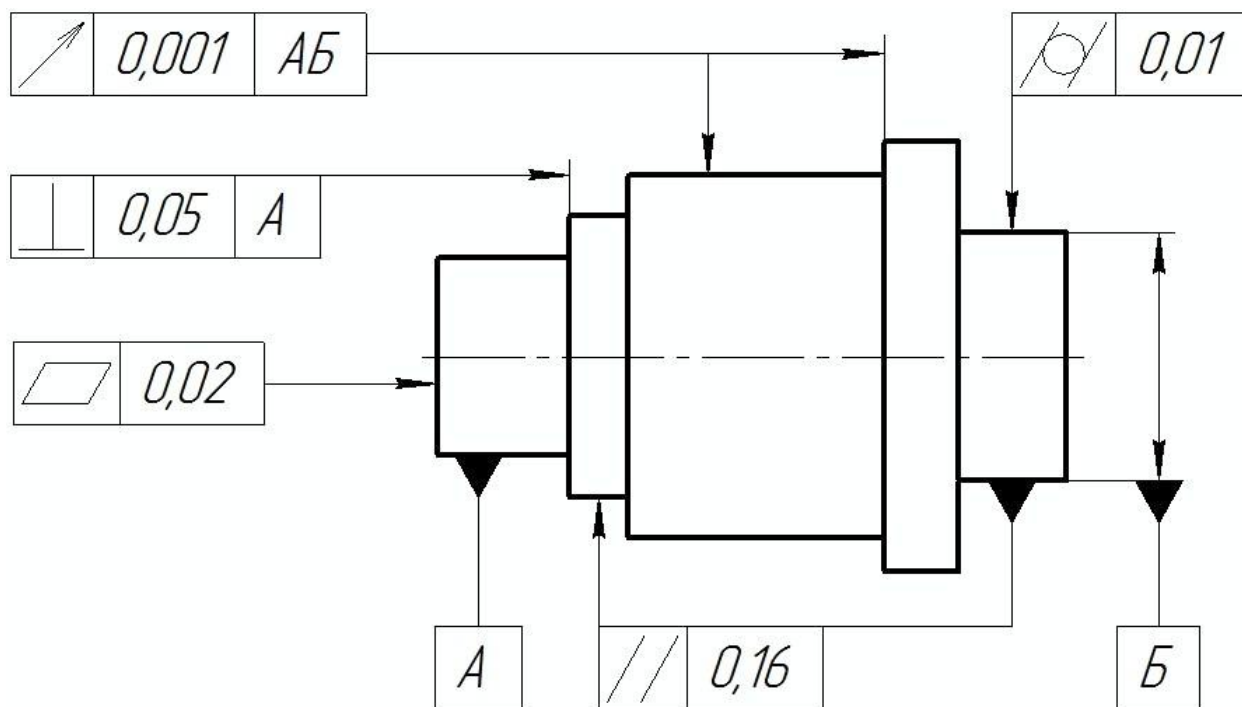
Примеры указания на чертежах допусков формы и расположения
